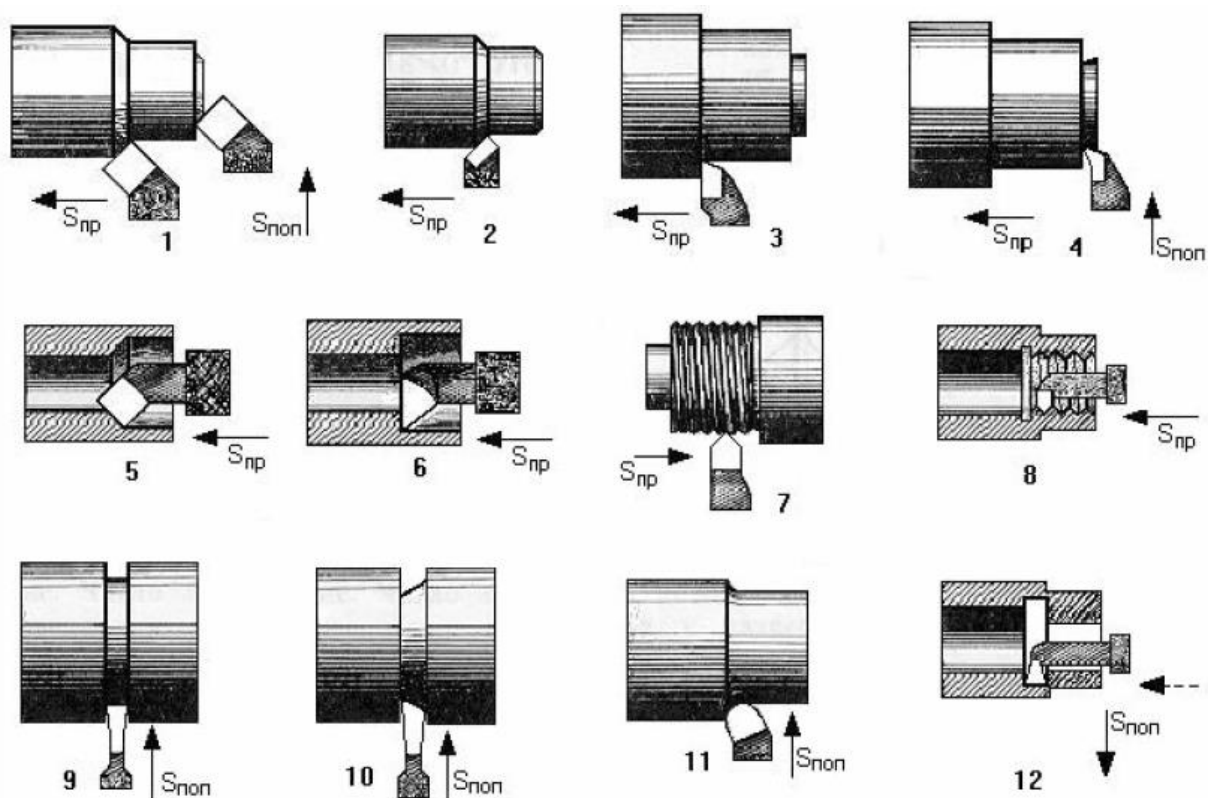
Типы токарных резцов и основные виды работ:
